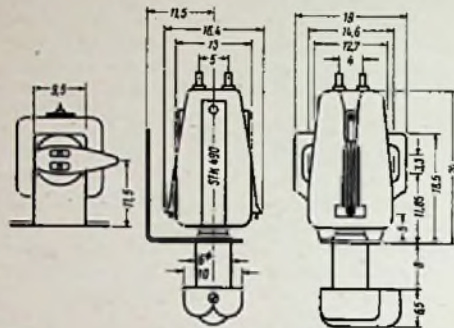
Einbaumaße des STK 490 bei Verwendung des Standard-Einbauminkeles
